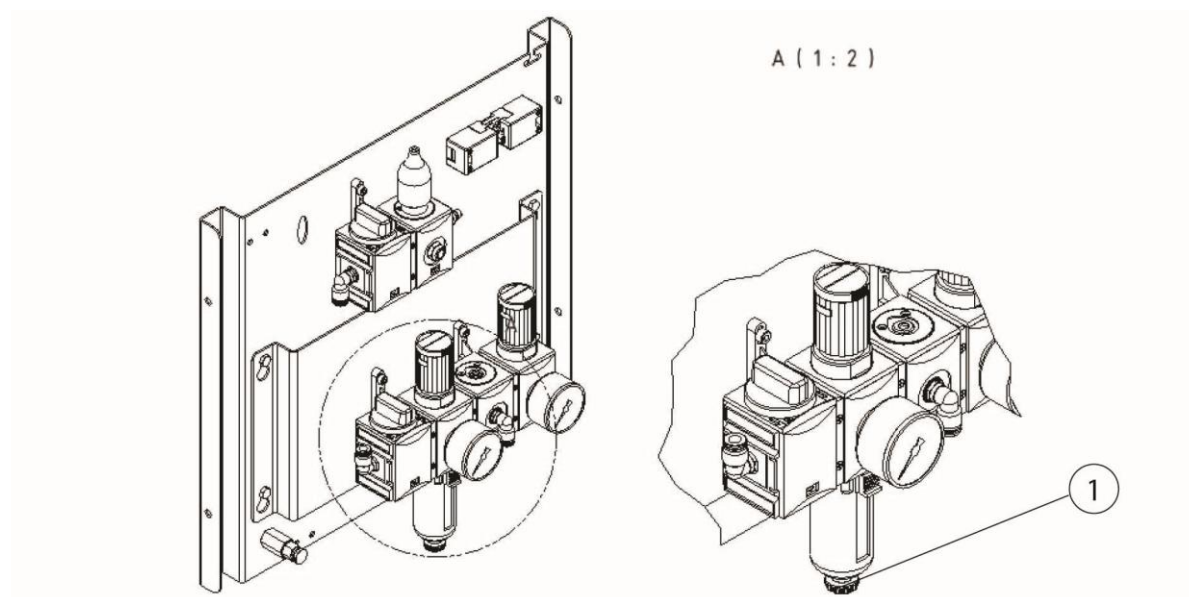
Вентиль слива конденсата узла подготовки воздуха
